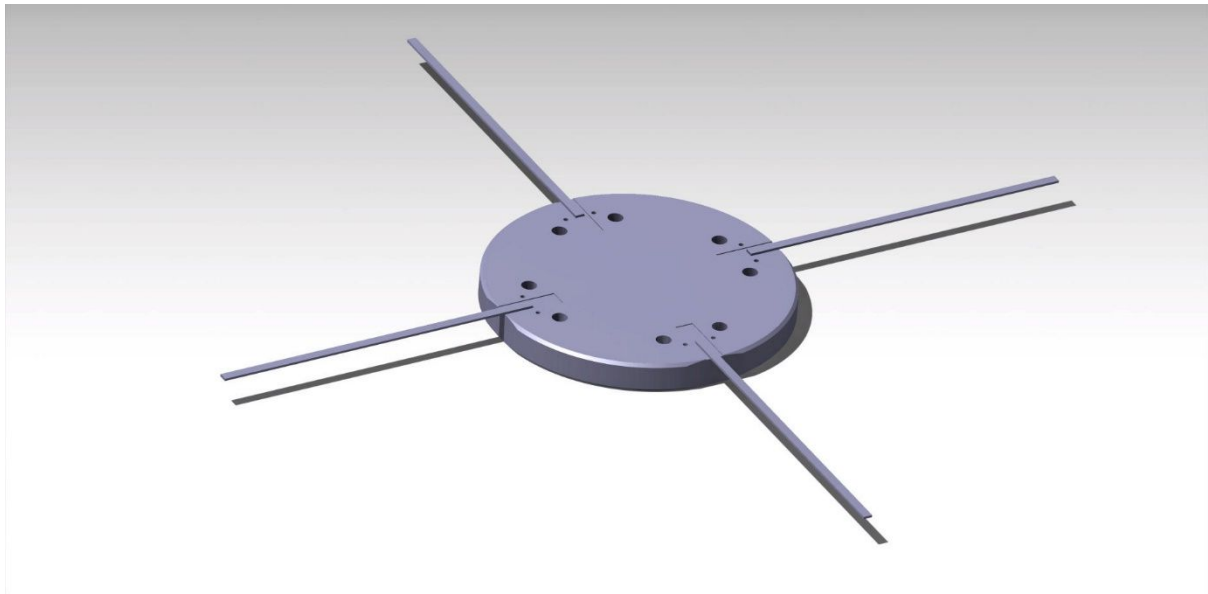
Table d'assemblage avec les 4 poutres qui la maintiennent.
